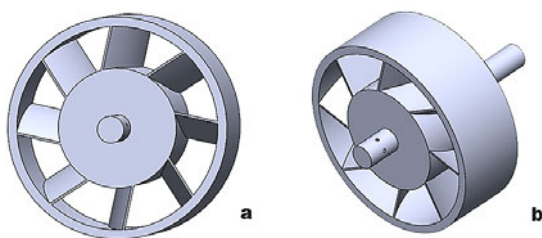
Swirler optimizado con inyector de combustible: (a) vista frontal; (b) vista isométrica.
